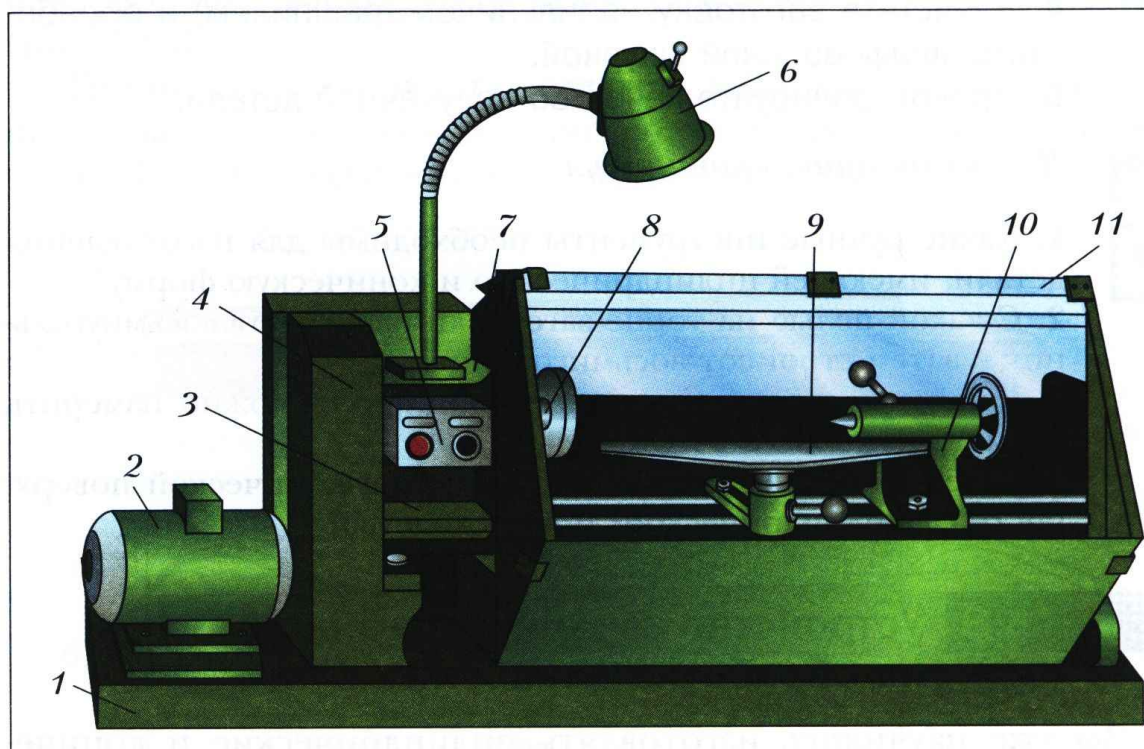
Токарный станок для обработки древесины: 1 – основание (стол); 2 – электродвигатель; 3 – станина с направляющими; 4 – ограждение ремённой передачи; 5 – кнопочный выключатель; 6 – светильник; 7 – передняя бабка; 8 – шпиндель; 9 – подручник; 10 – задняя бабка; 11 – защитный экран
